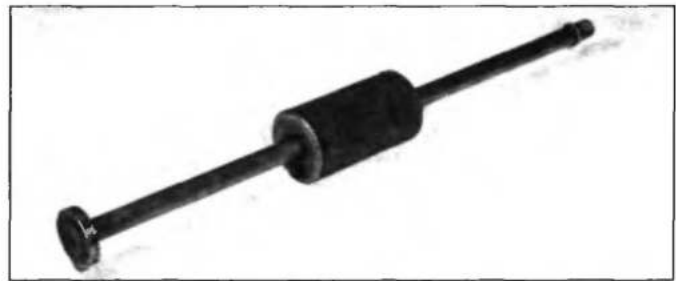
Ударник - приспособление для выпрессовки (запрессовки) втулок и подшипников ударным способом
